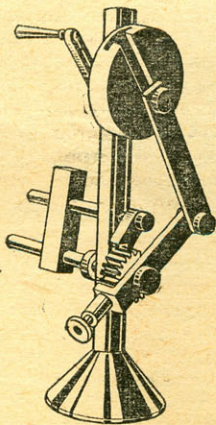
Действующая модель кинематической схемы механической подачи стола поперечно-строгального станка.
